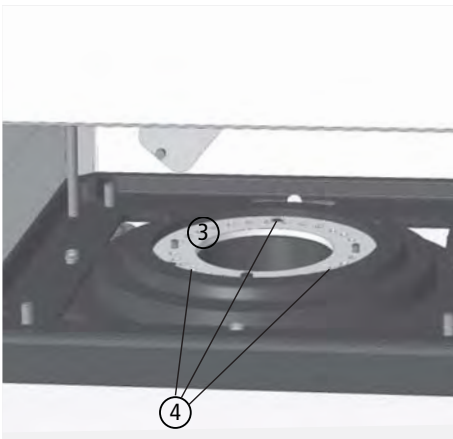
Démontez la rondelle de réglage des butées latérales
